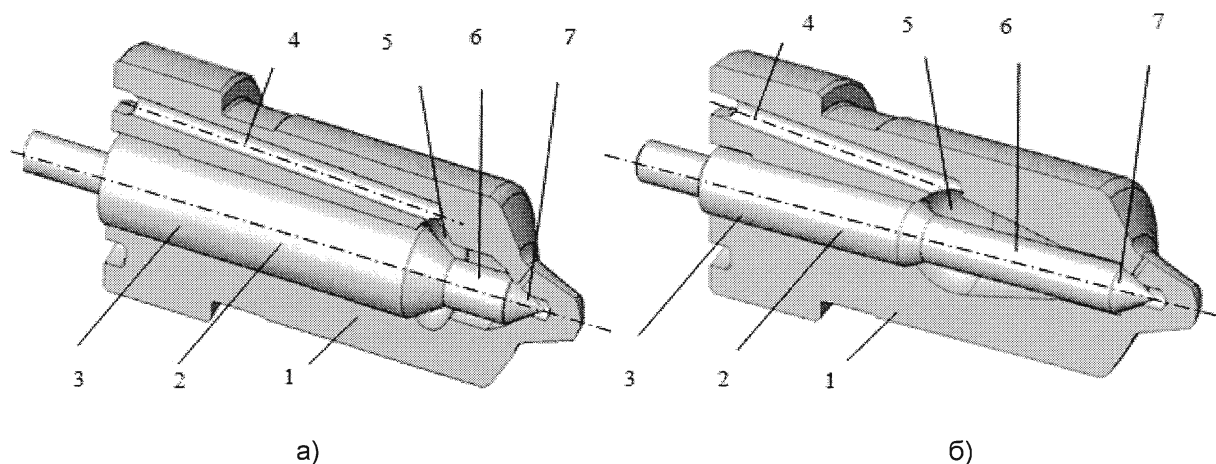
Штатный (а) и опытный (б) распылители типа DLA: 1 – корпус, 2 – игла, 3 – направляющее сопряжение, 4 – каналы в корпусе, 5 – полость корпуса, 6 – стержень иглы, 7 – запирающее сопряжение
